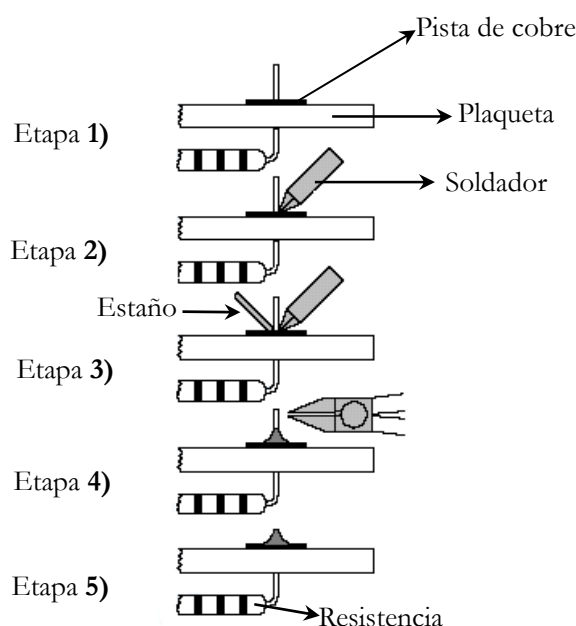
Pasos a seguir para lograr una buena soldadura.
